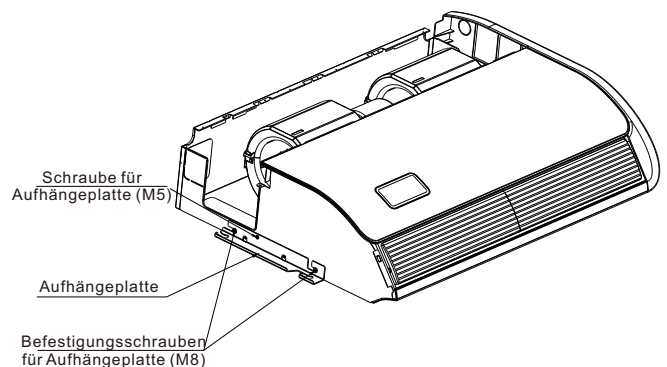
Aufhängungsbolzen und Muttern
